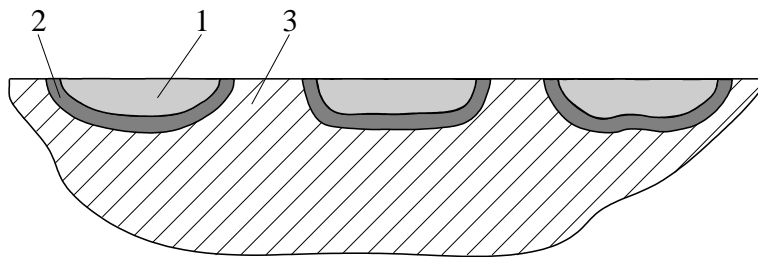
Дискретное упрочнение коленвала двигателя типа Д80
